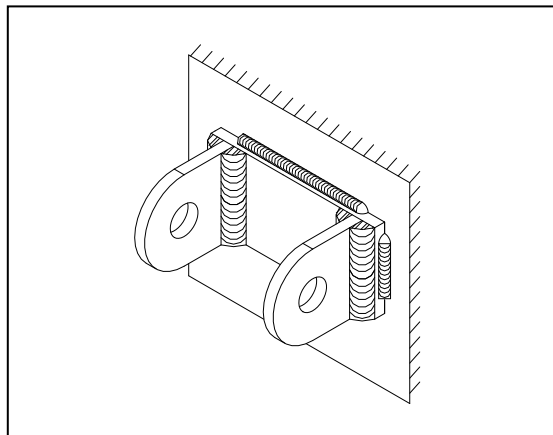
Disposición soldadura anclaje de suspensión
